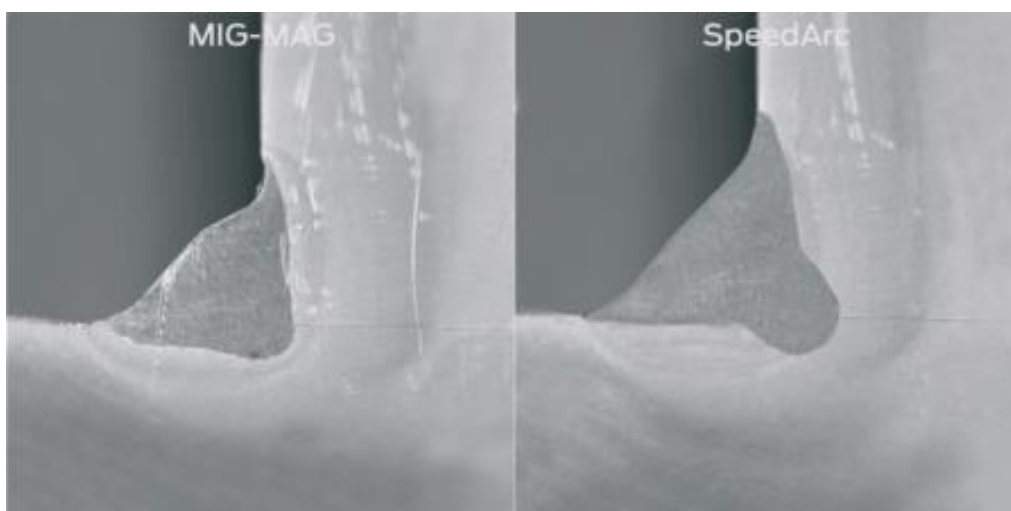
Более глубокий провар – меньше проходов сварки [4]
